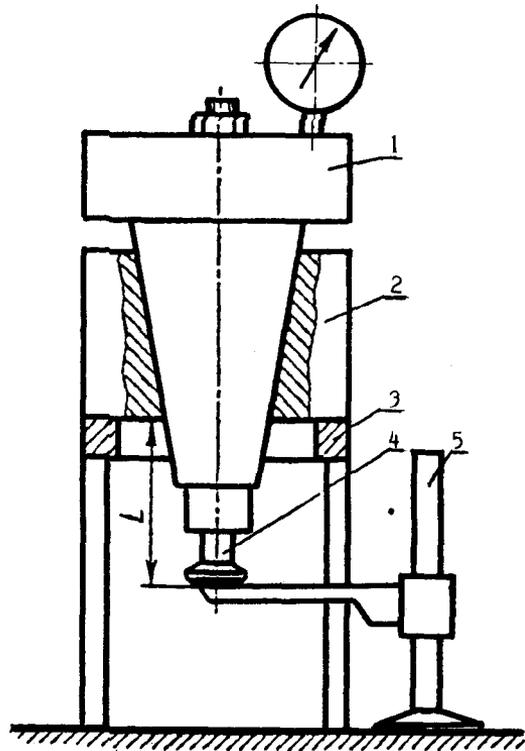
Приспособление для контроля тарельчатых пружин:
